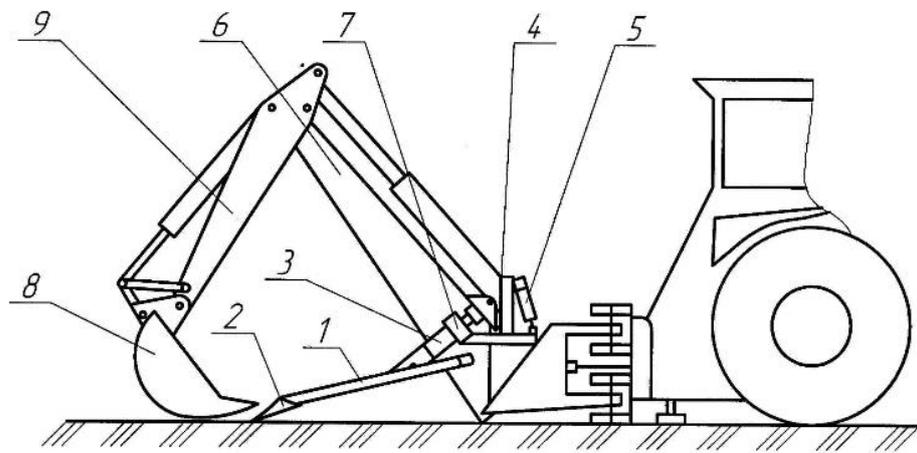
Очиститель ковша оборудования обратной лопаты:
